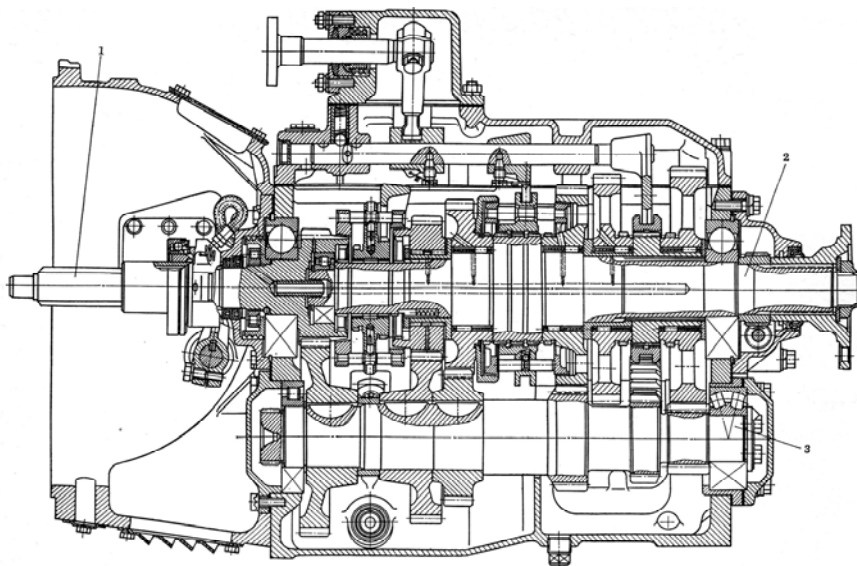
Коробка передач автомобиля КамАЗ-4310:
